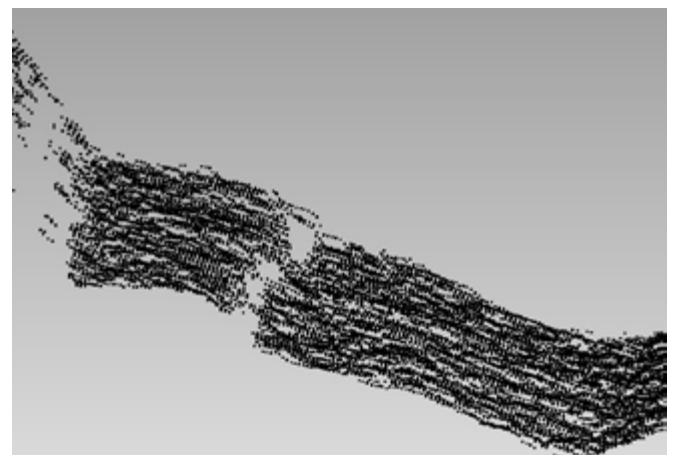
Messung einer Schweißnahtprobe, welche sich im Wasser befindet. Die Navigation erfolgt an der Luft.
